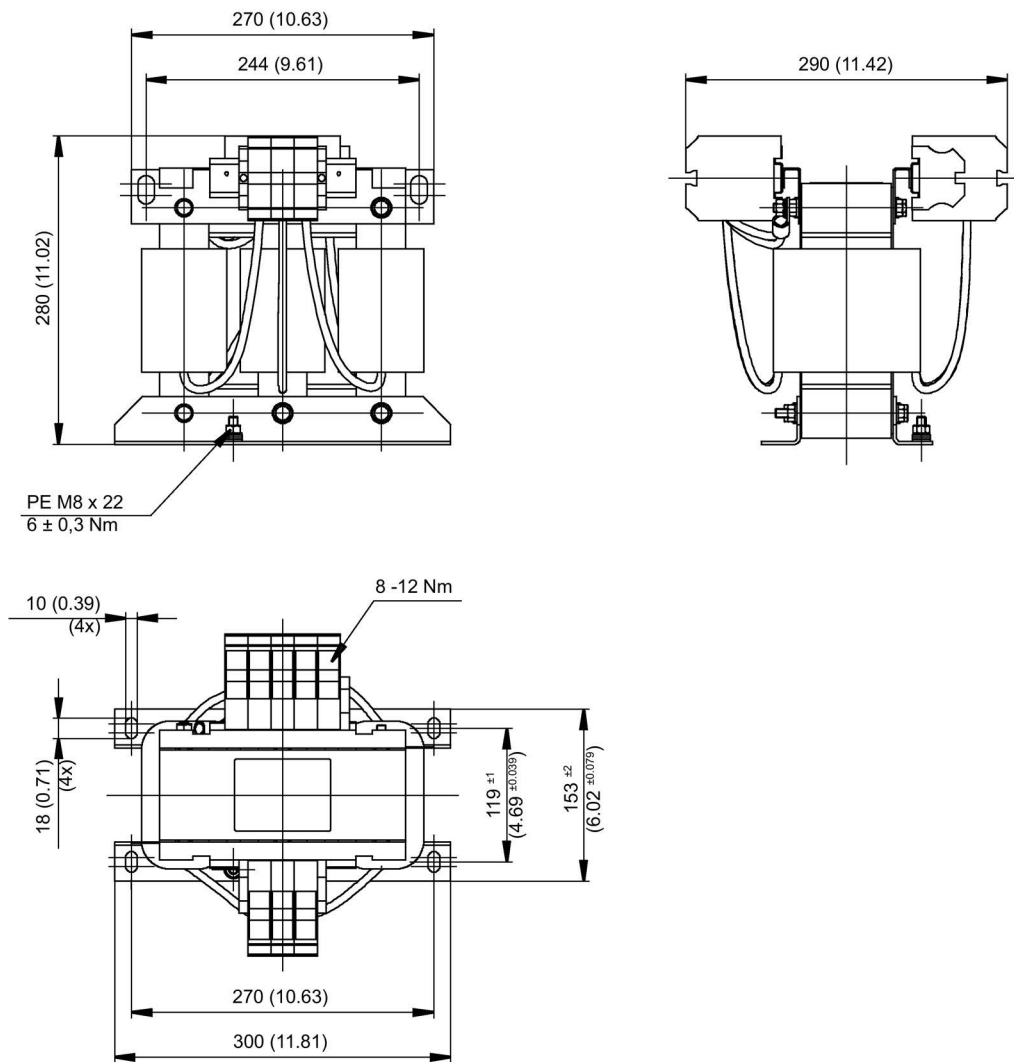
Croquis acotado de una bobina de red para Smart Line Module de 55 kW, todas las medidas en mm y (pulgadas)
